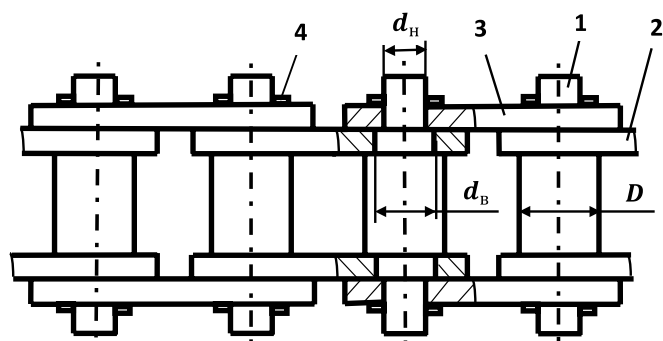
Фрагмент приводной пластинчатой цепи [10] со ступенчатыми валиками
